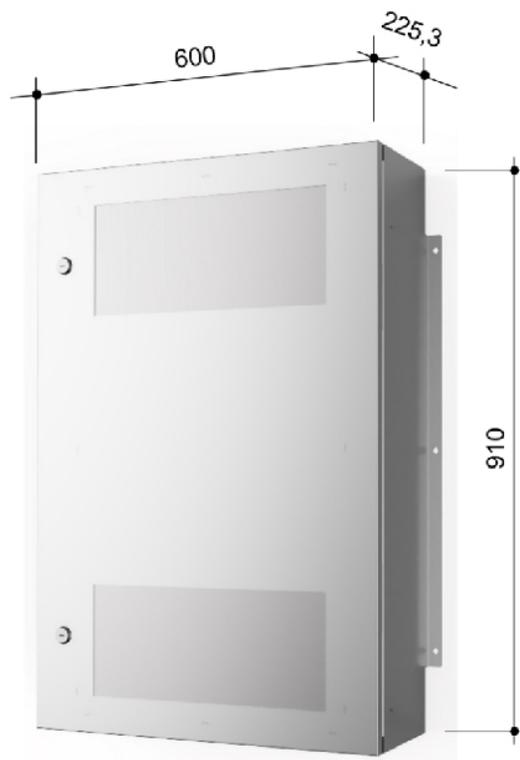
Gehäuse Wechselrichter – Abmessungen
